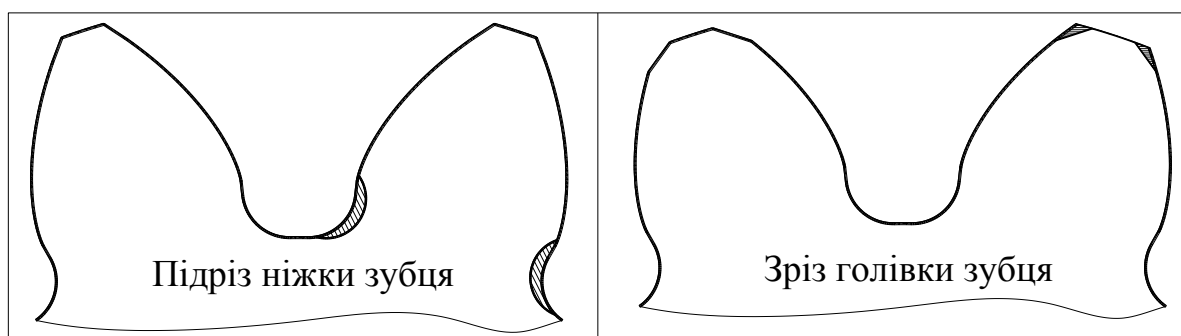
Підріз ніжки і зріз голівки зубця
